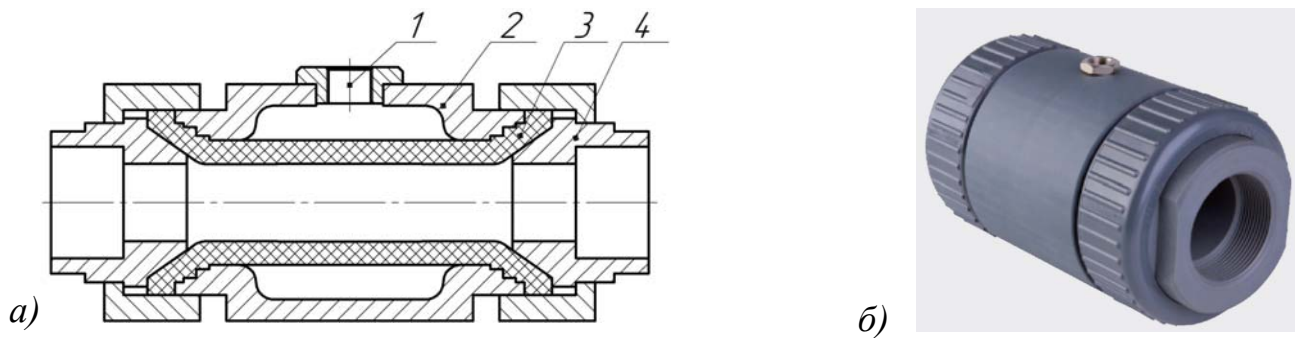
Пневматичний шланговий затвор: конструкція (а), де 1 – патрубок подачі стисненого повітря; 2 – корпус; 3 – патрубок з еластичного матеріалу; 4 – фланець; загальний вигляд (б)
